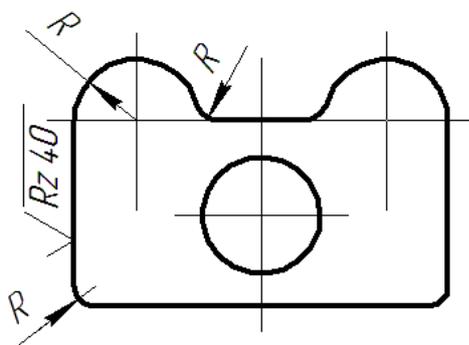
Обозначение шероховатости поверхностей плавно переходящих одна в другую
